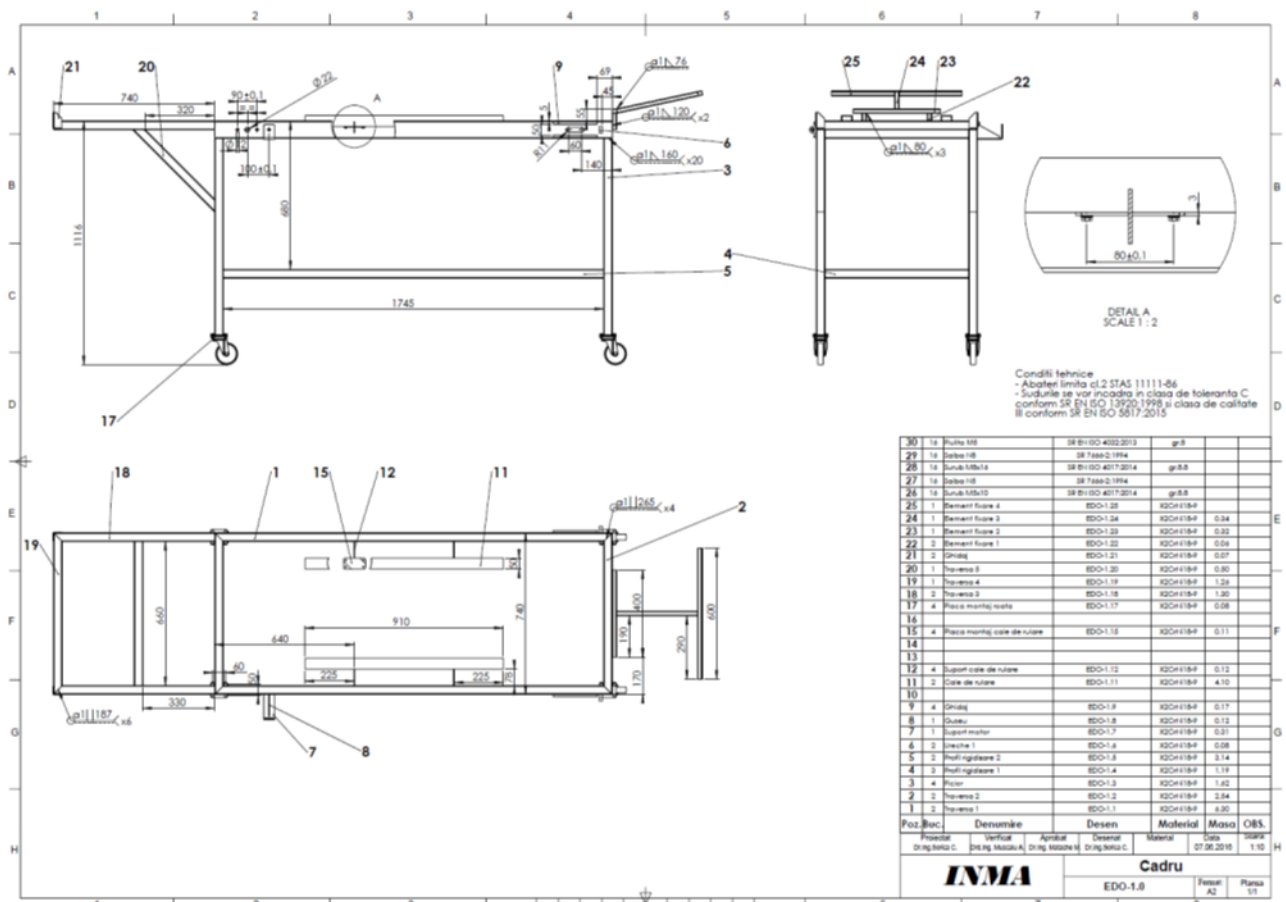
Desen de ansamblu EDO-1.0 – Cadru
